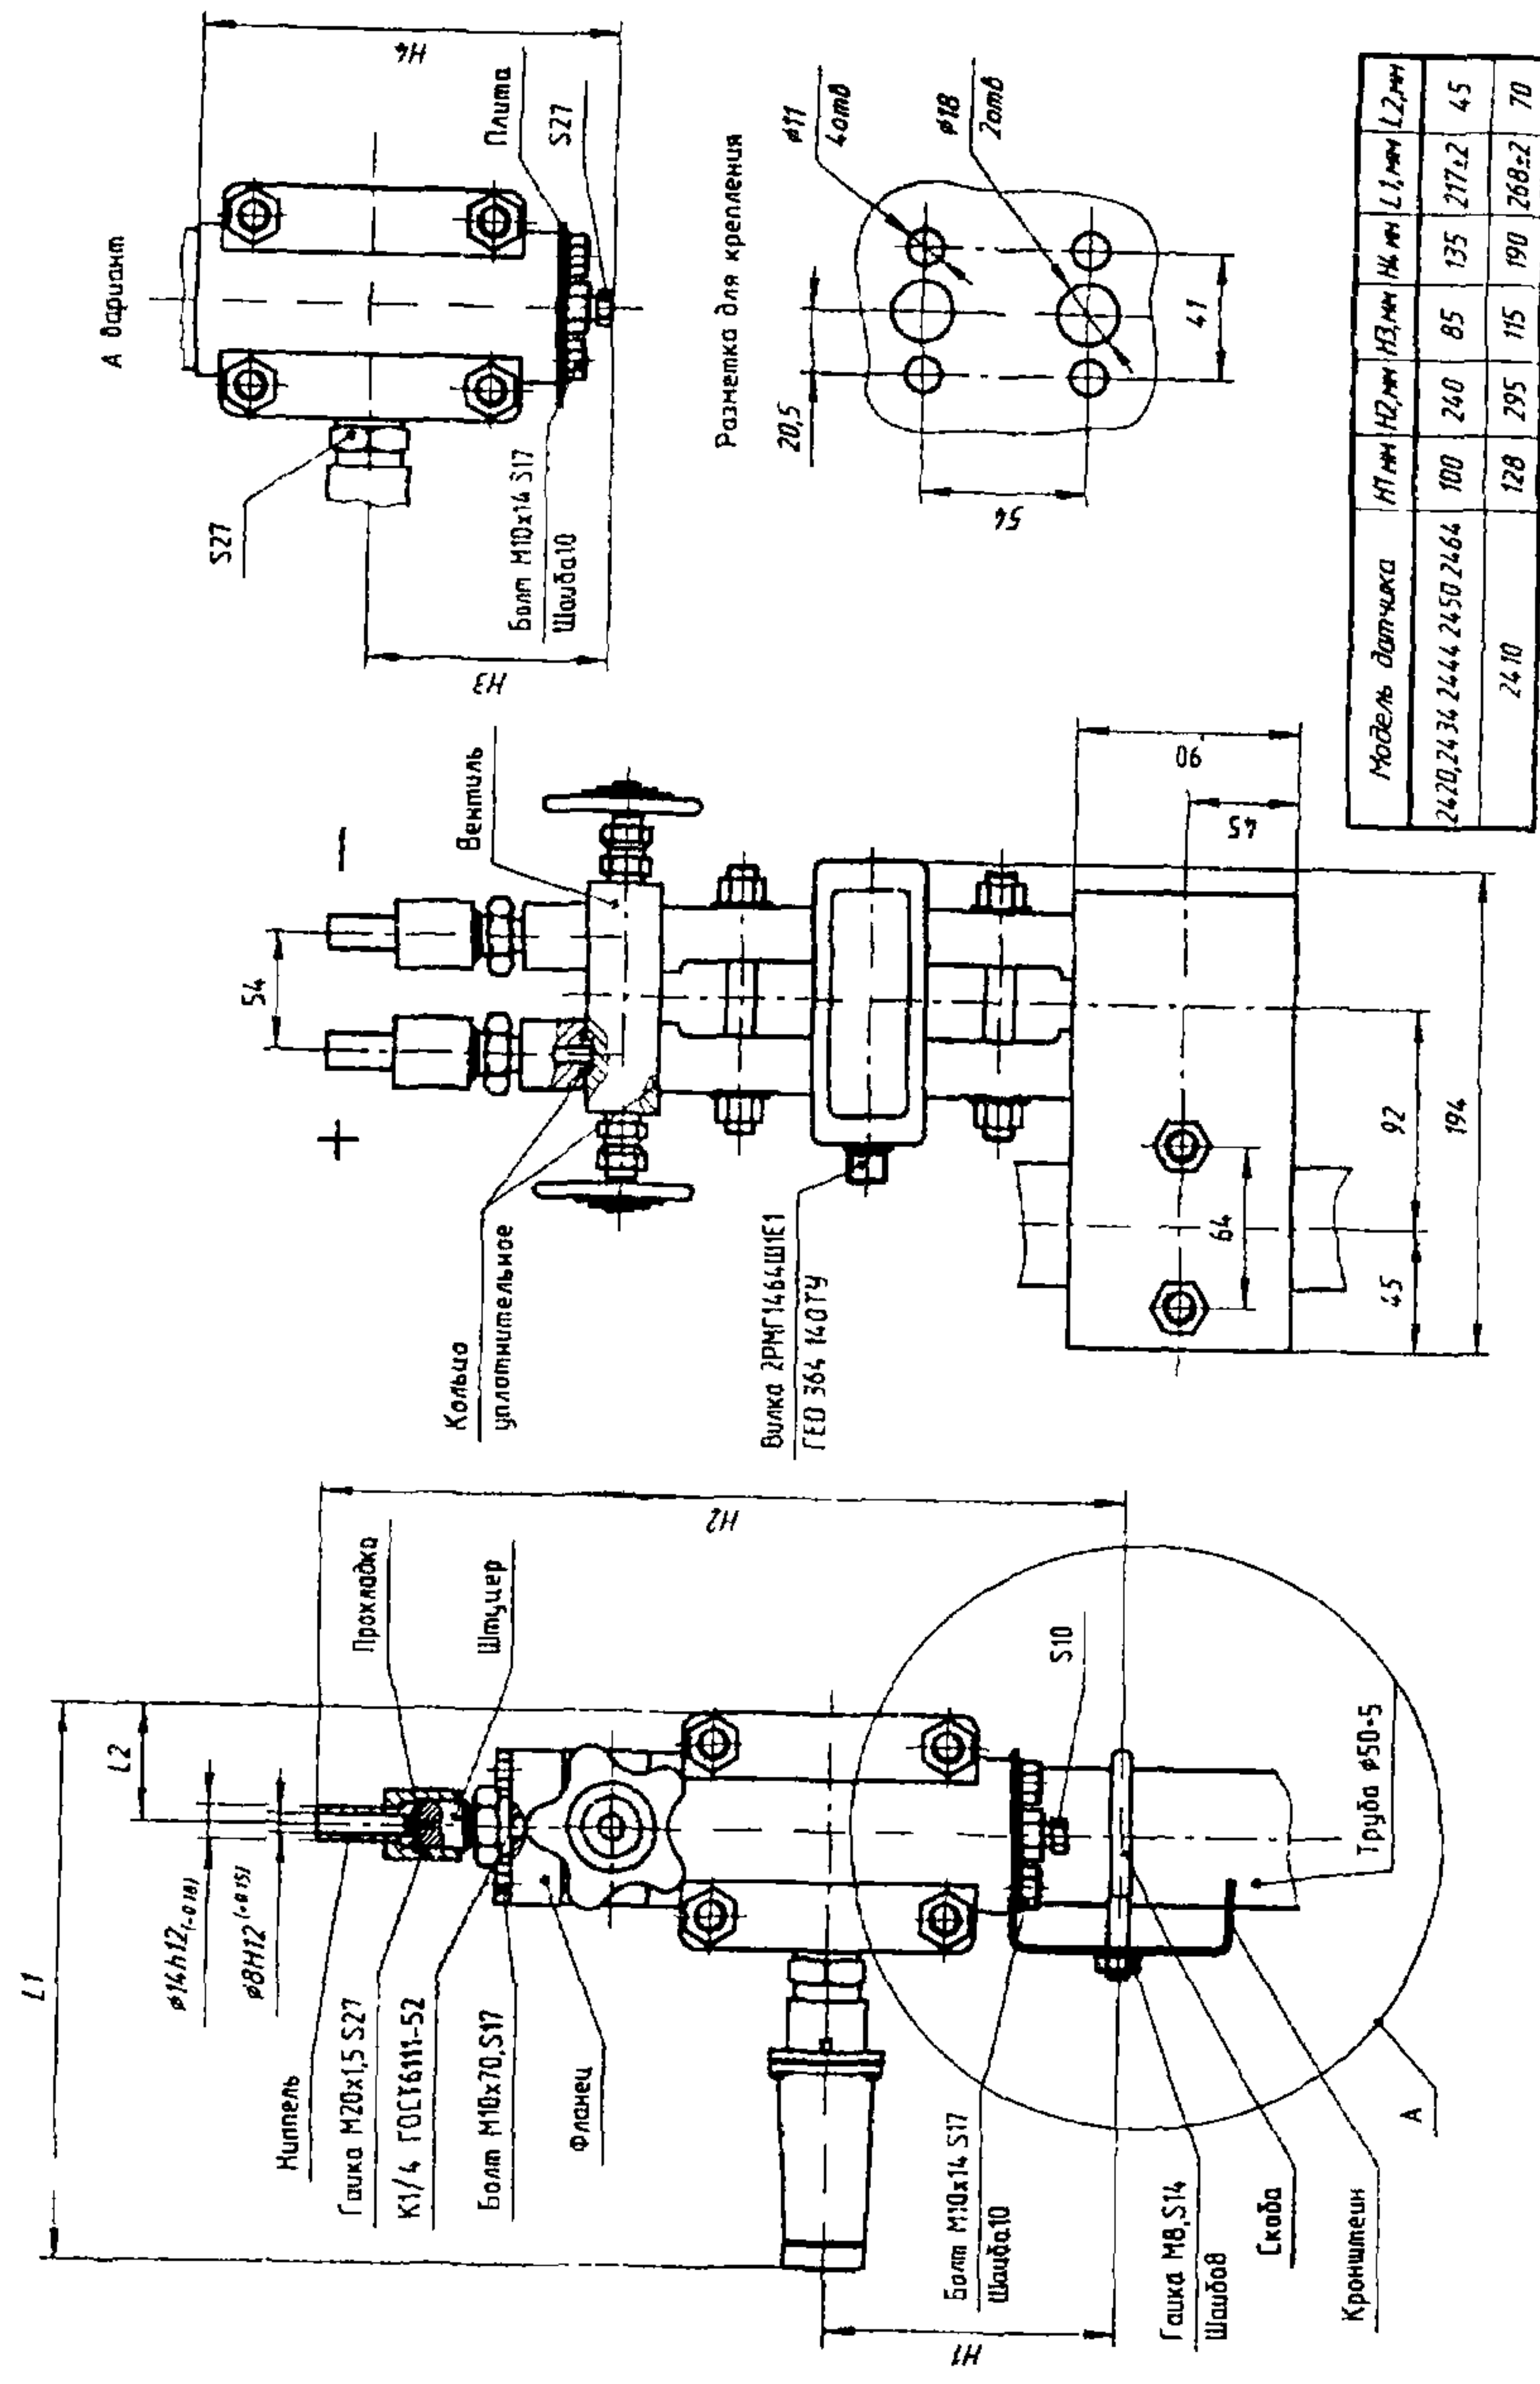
Установочные и присоединительные размеры датчиков моделей 2410, 2420, 2434, 2444, 2450, 2464 с установленным вентиляльным блоком, ниппелями под накидные гайки
